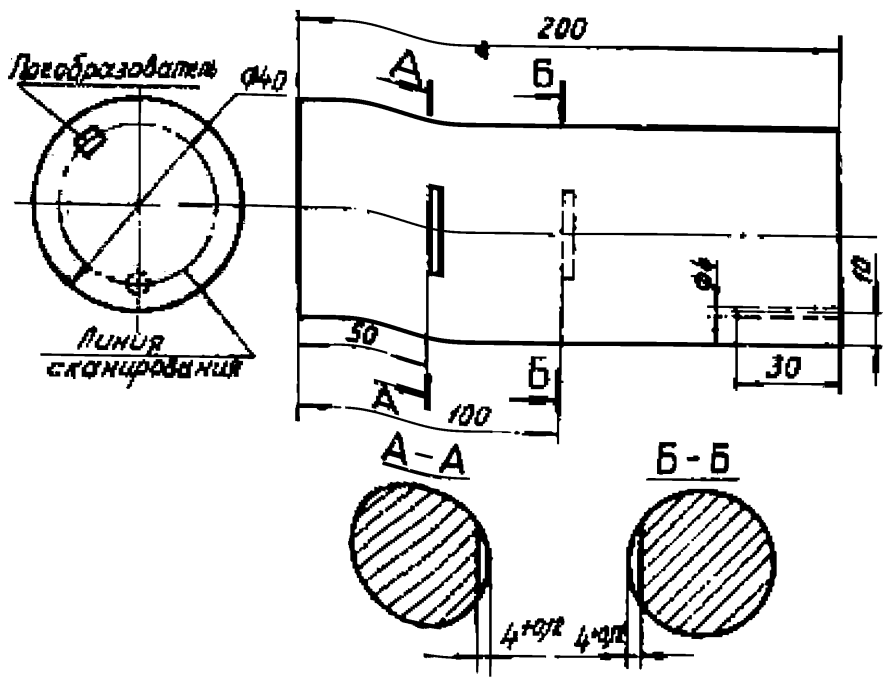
Стандартный образец для настройки ультразвукового прибора при НК элеваторов
